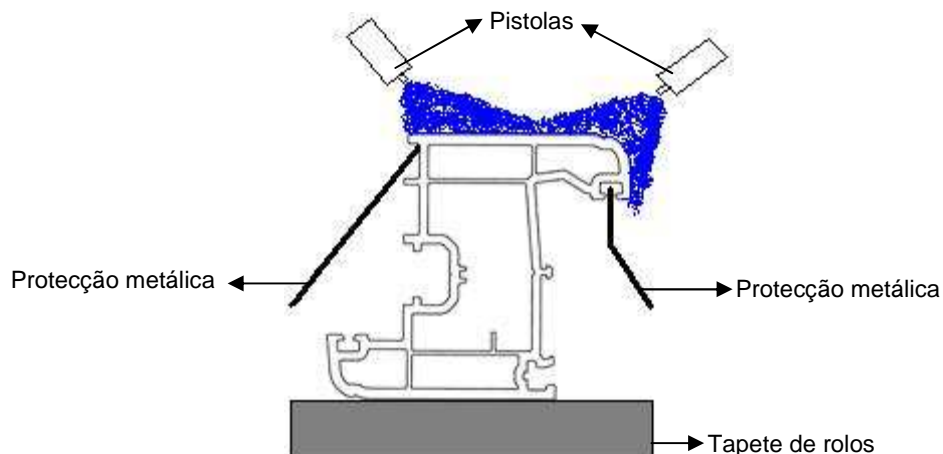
Perfil P3051 a ser pintado durante a etapa 4 da máquina B.
